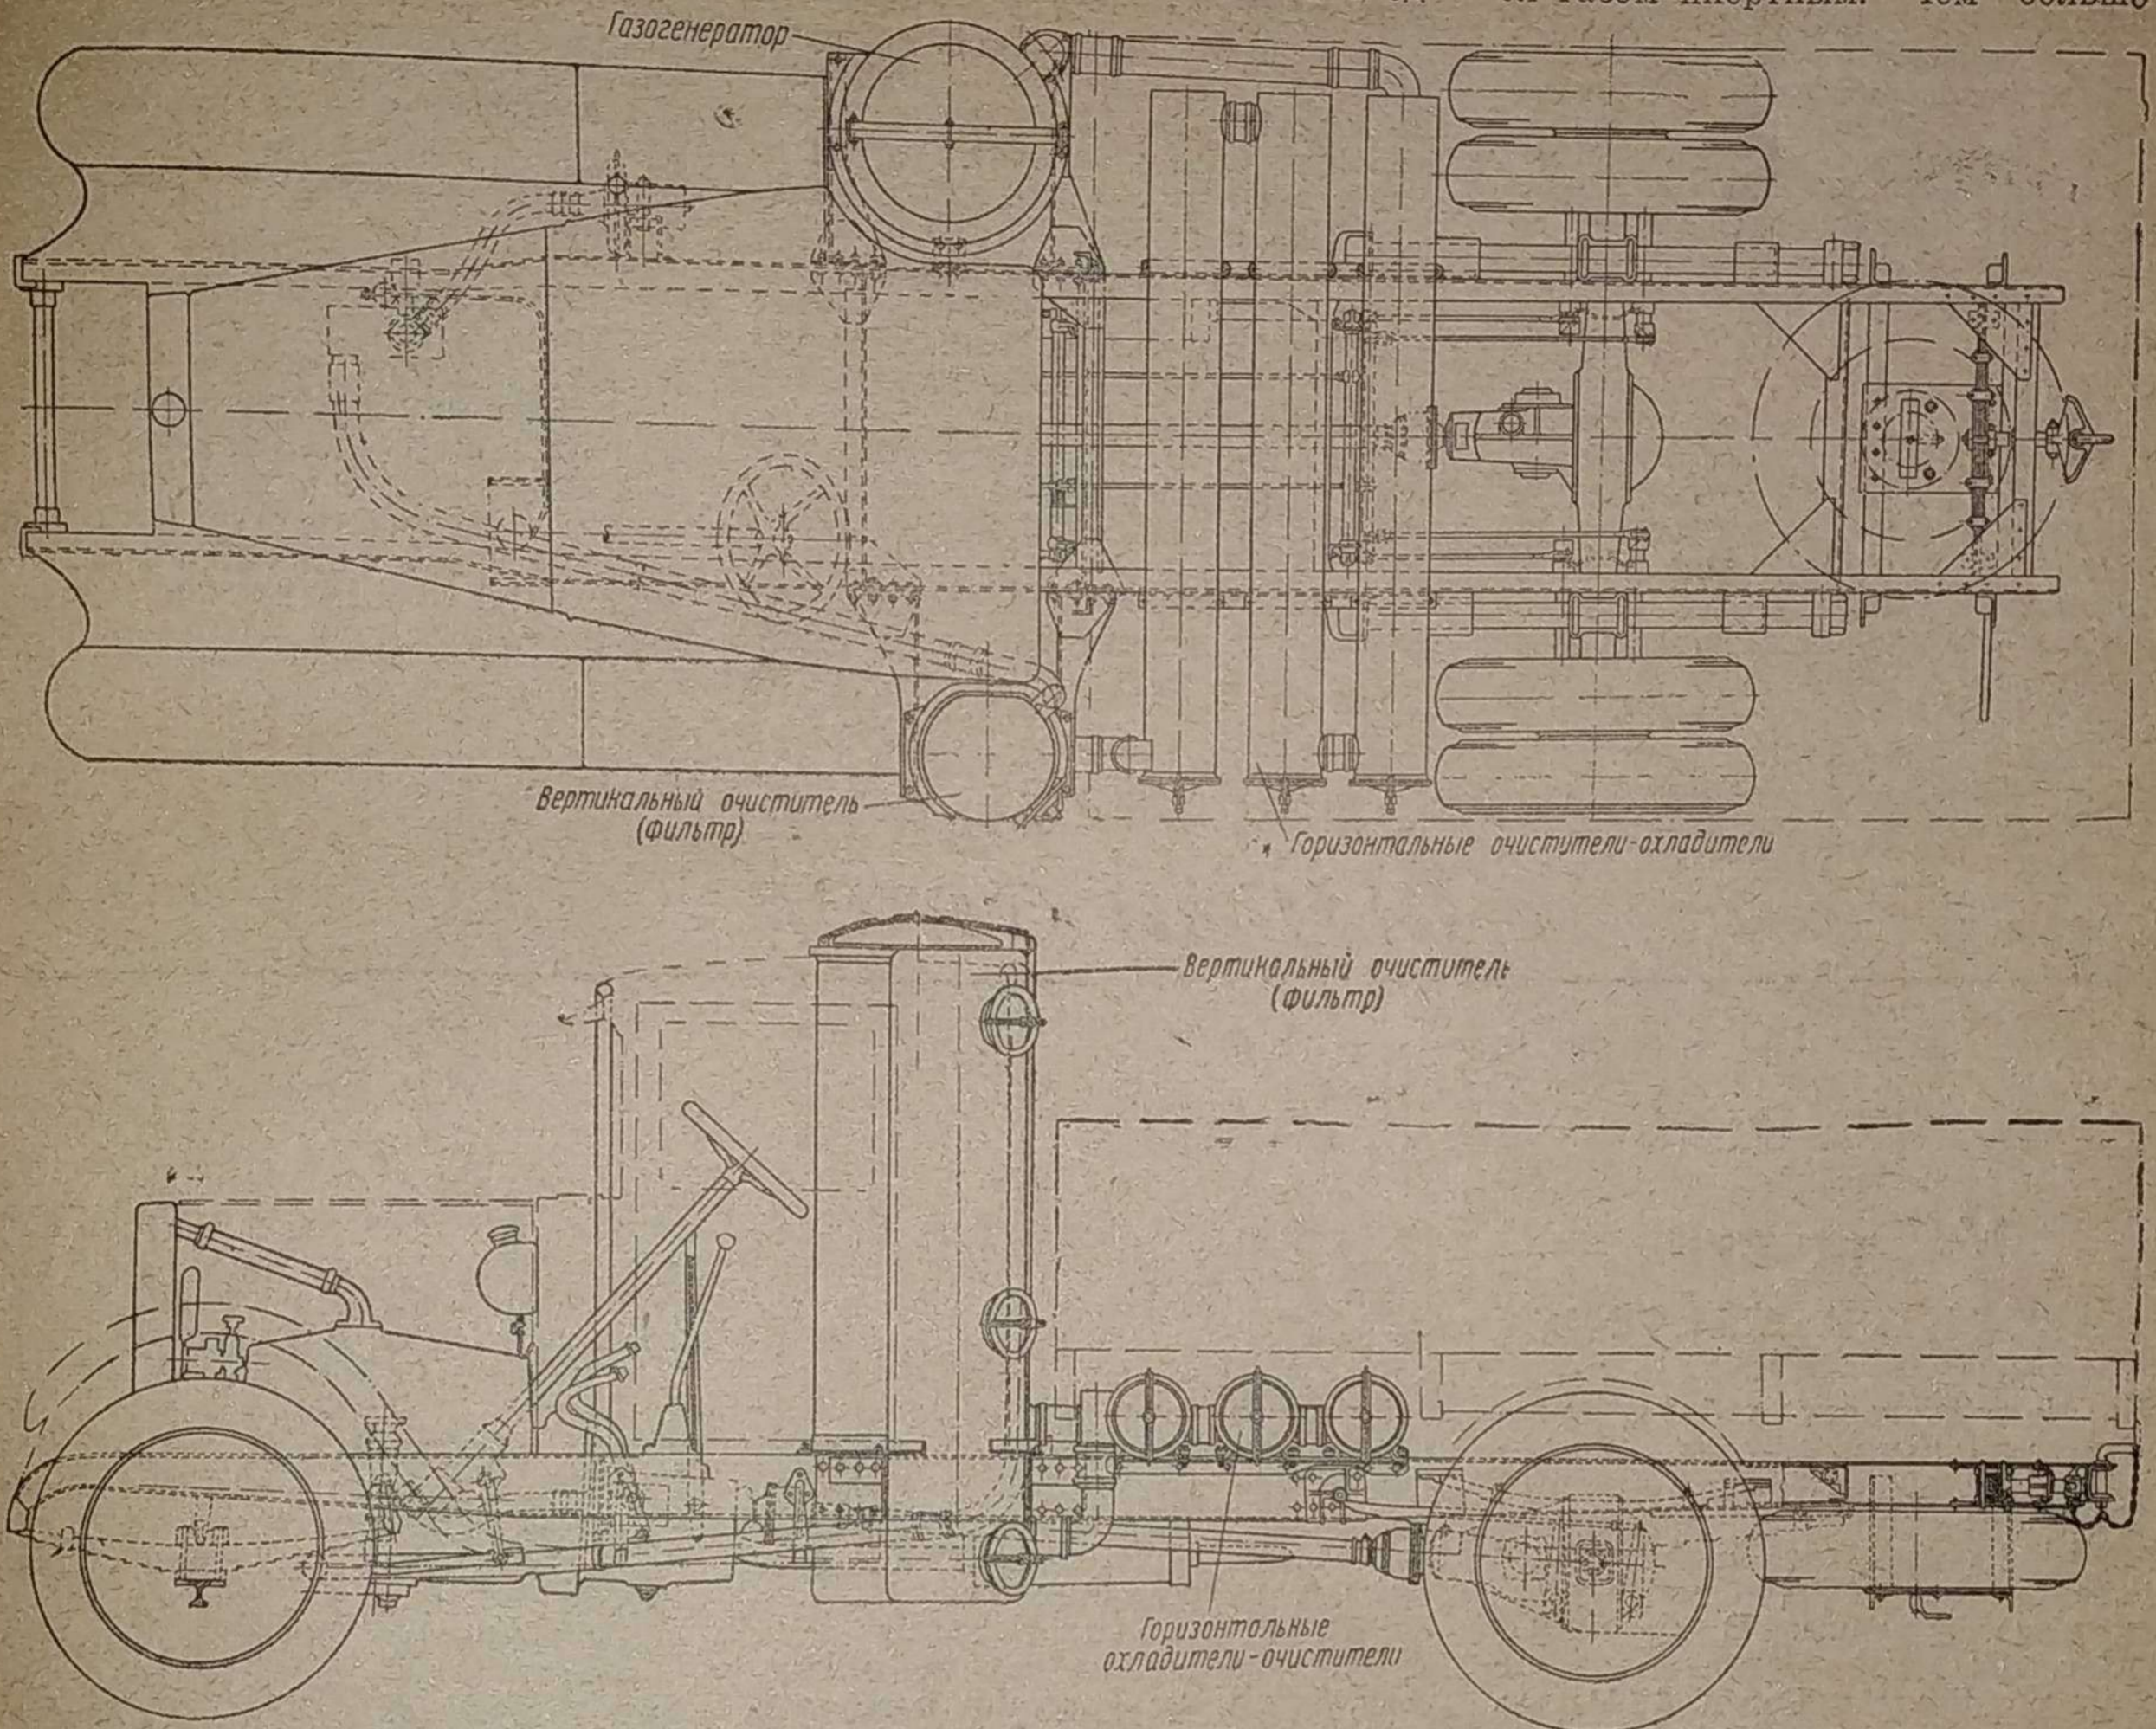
Грузовой газогенераторный автомобиль ЗИС-21 (сверху — план; снизу — вид сбоку)
